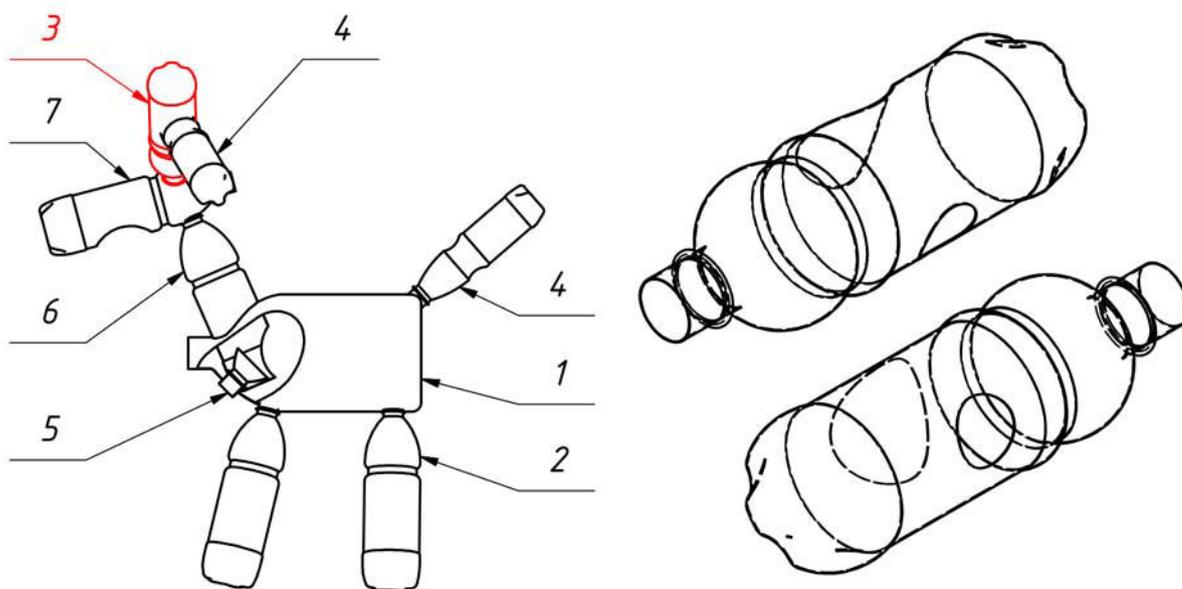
Подготовка деталей «основания рогов» (поз. 3)
